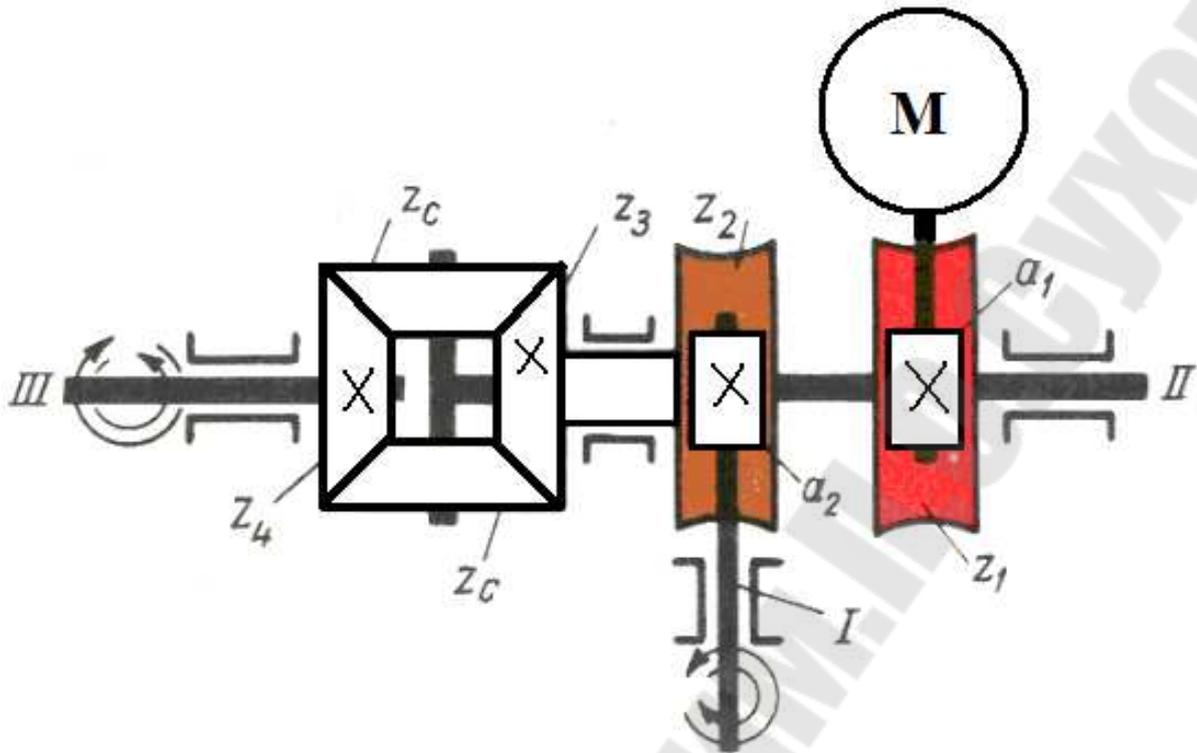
Схема планетарного механизма с коническими колёсами
